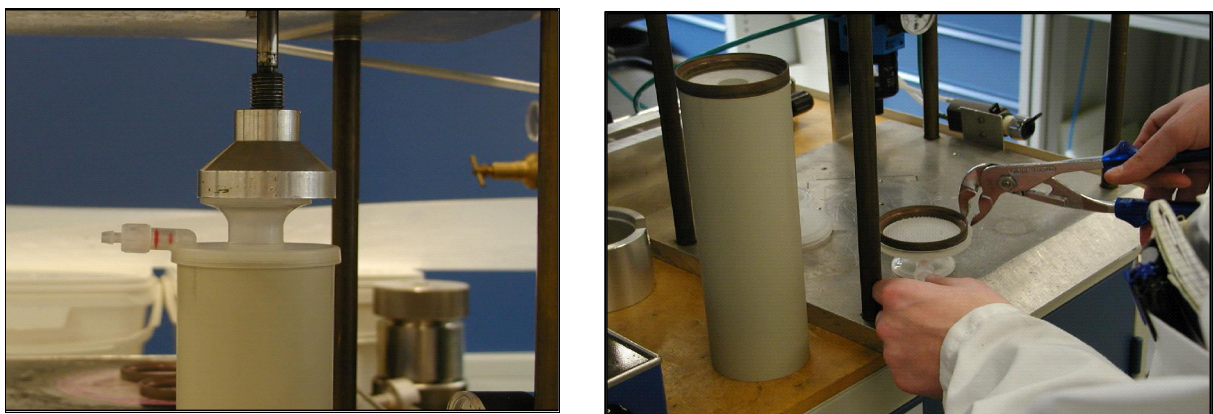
Capsule bauen. links: Aufschmelzen der Schweißkonturen des Rohres und der Gehäusekappe; rechts: Fügeprozess, Abkühlen der Schmelze erfolgt unter Anwendung einer definierten Fügekraft.
